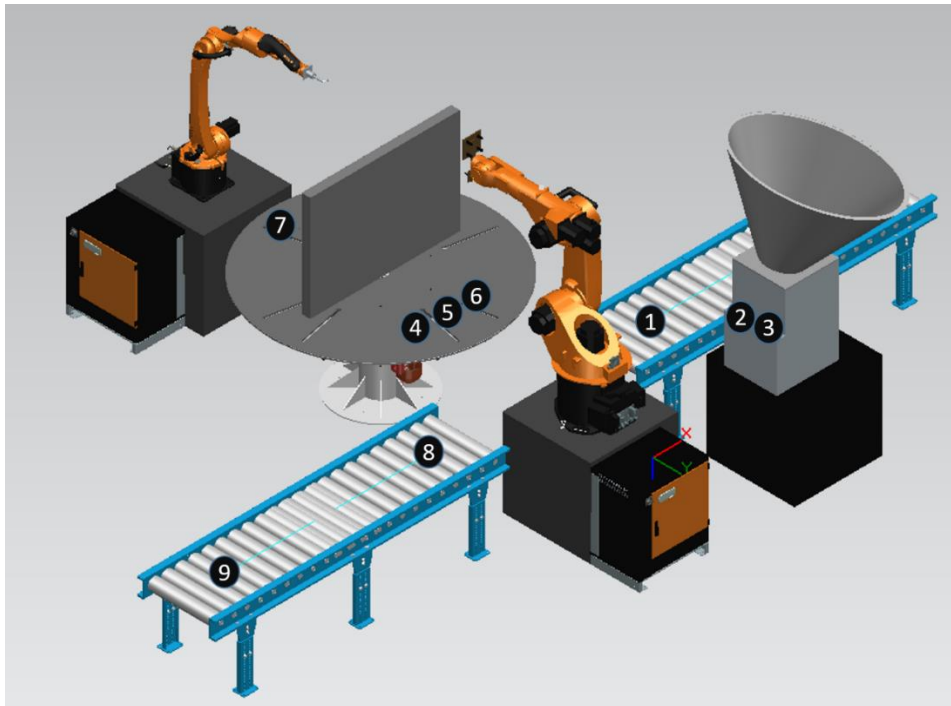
Posición de los sensores dentro de la célula de soldadura
